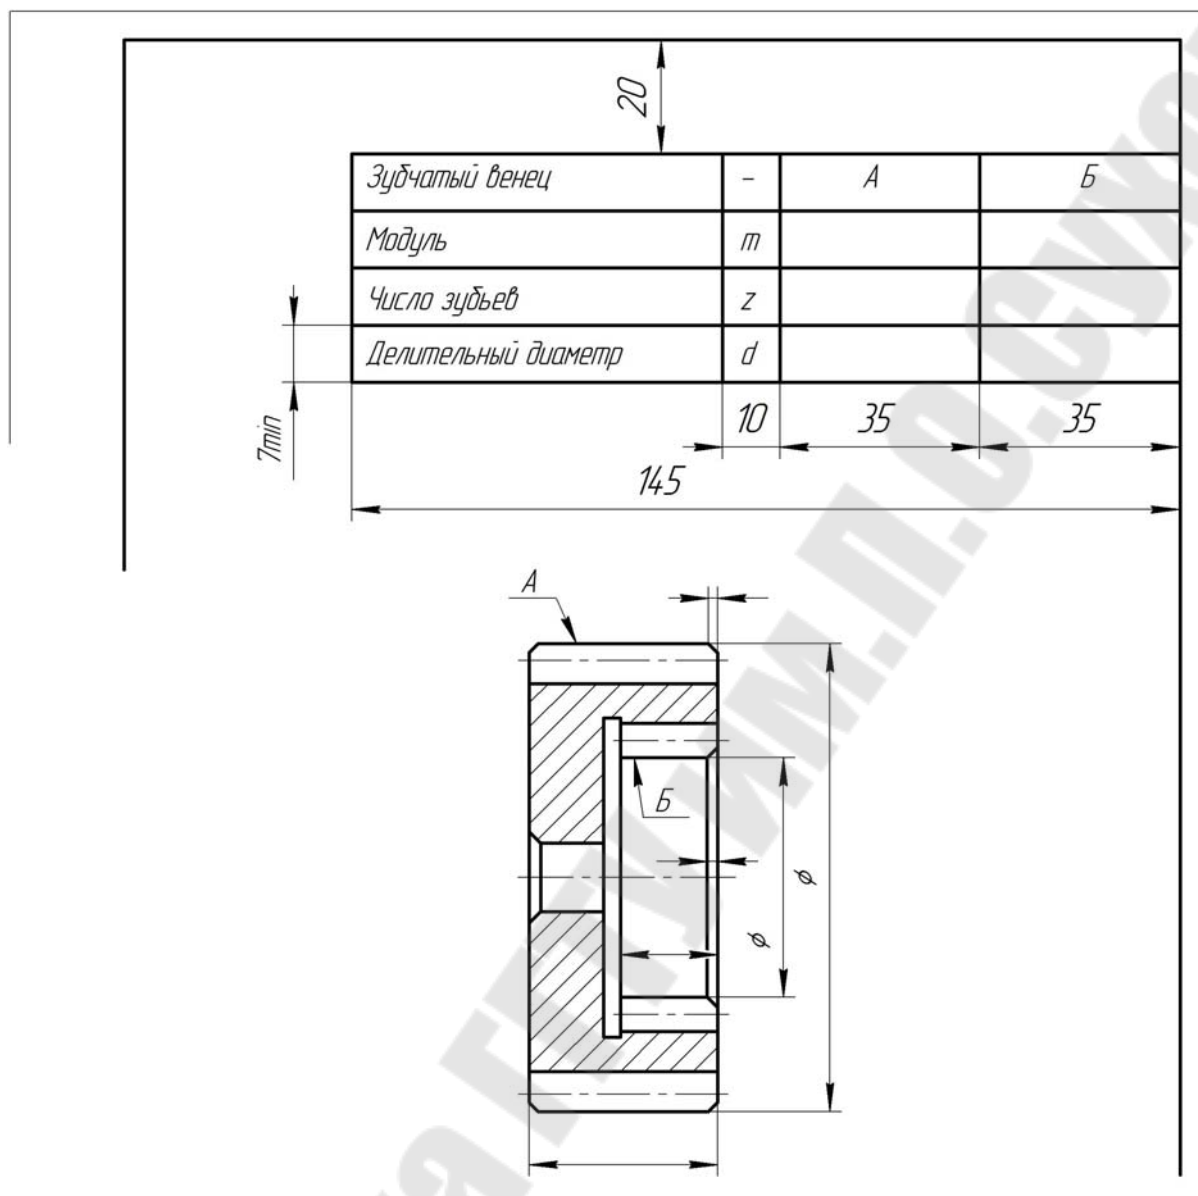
Цилиндрическое зубчатое колесо с двумя зубчатыми венцами
